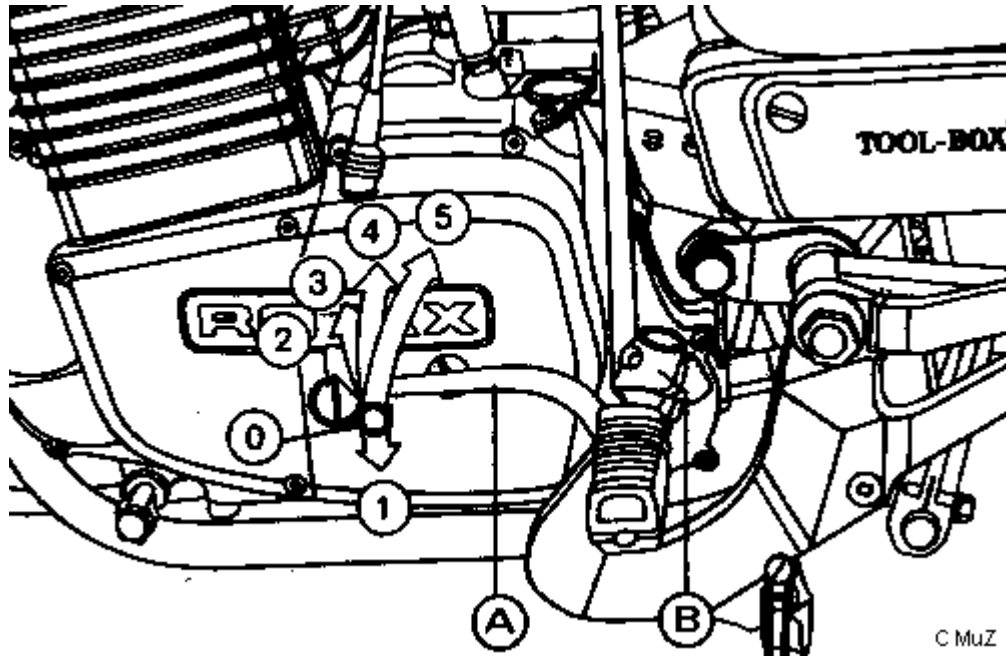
Fußschaltung Zahlen: Lage der Gänge, (A) Fußschalthebel (B) Kickstarter
